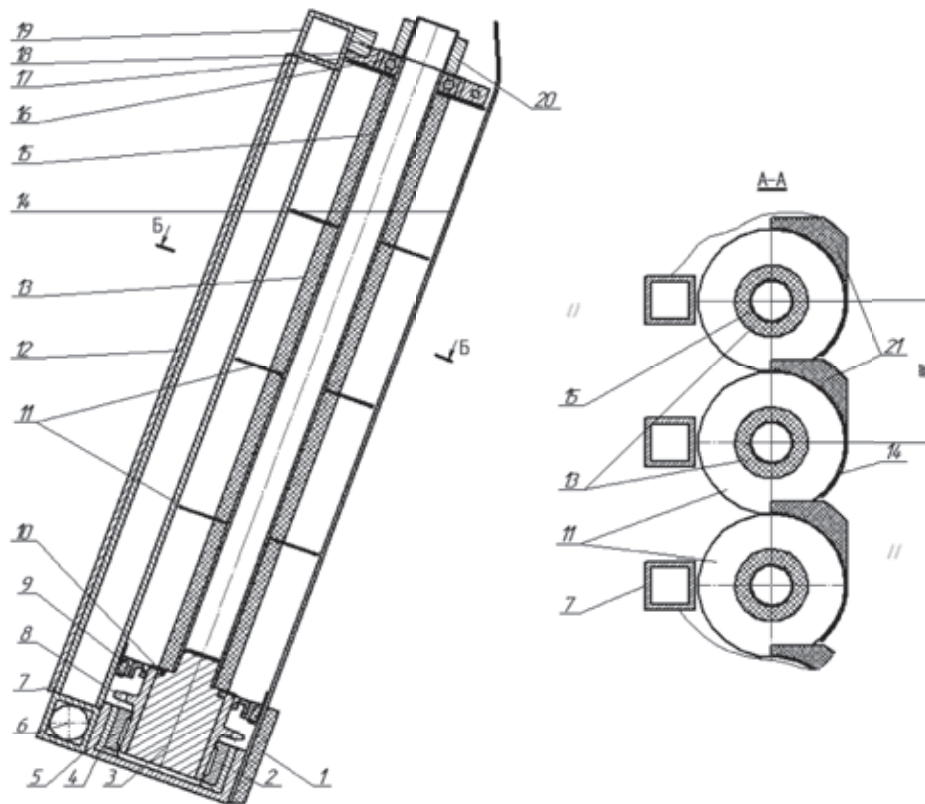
Дисковое режущее устройство: 1 – подушка; 2 – подшипник игольчатый; 3 – основание вала; 4,17 – стакан; 5 – кронштейн нижний; 6 – ось; 7 – корпус; 8 – звездочка; 9 – манжета; 10 – уплотнительное кольцо; 11 – абразивный диск; 12 – стенка задняя; 13 – втулка; 14 – передняя стенка; 15 – вал; 16 – подшипник шариковый; 18 – кронштейн верхний; 19 – каркас неподвижный; 20 – гайка; 21 – противорез
